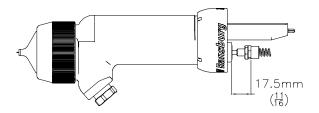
Dimensiones de la tuerca de ajuste del gatillo
